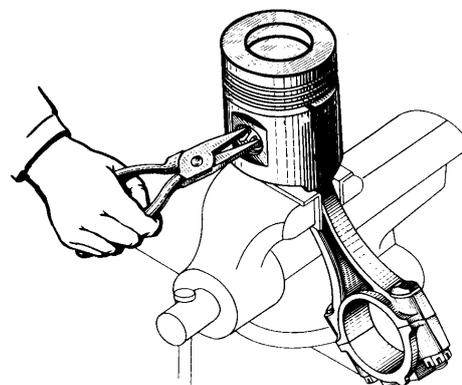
Демонтаж стопорного кольца поршневого пальца
